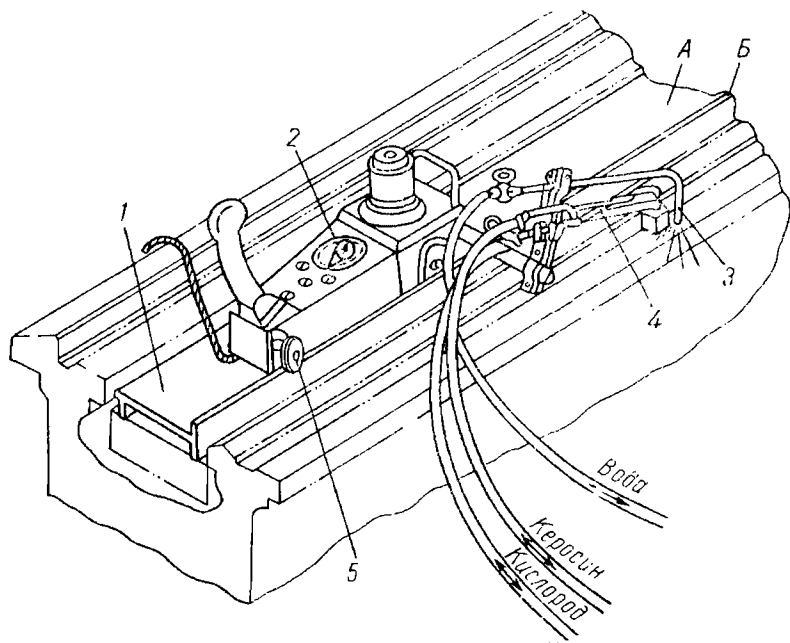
Передвижная установка для поверхностной закалки направляющих станин
